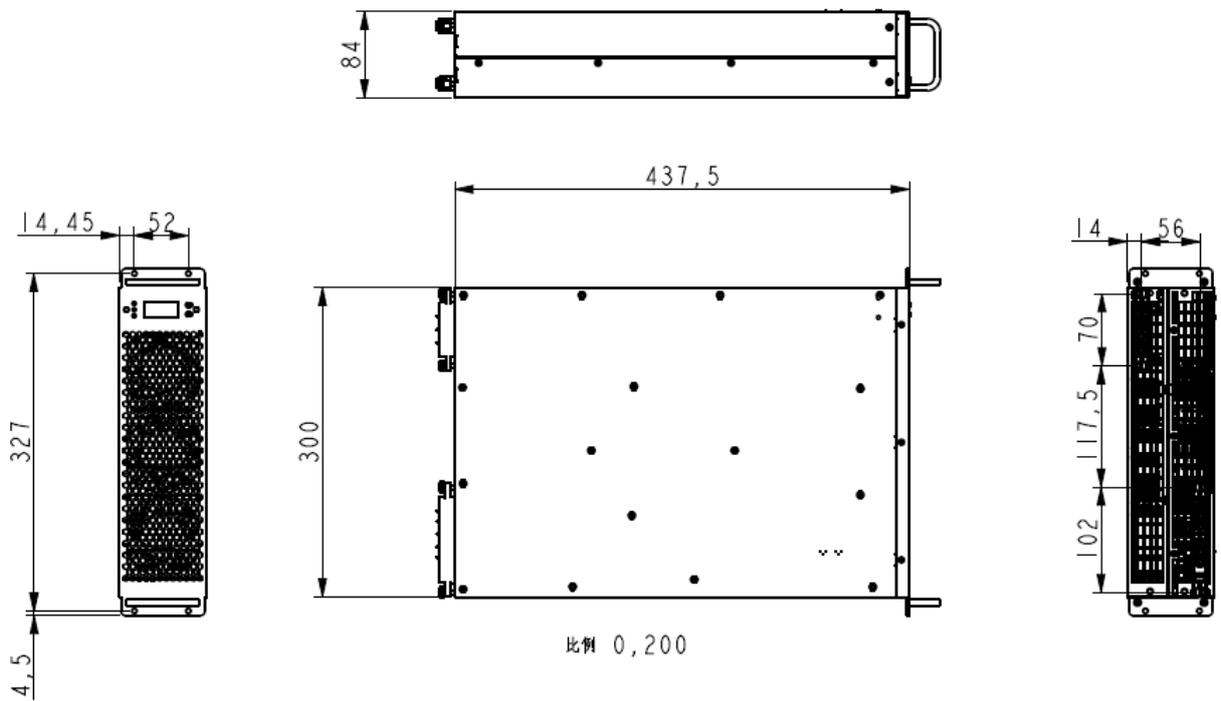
모듈 가로 배치 사이즈 (단위 : mm)
